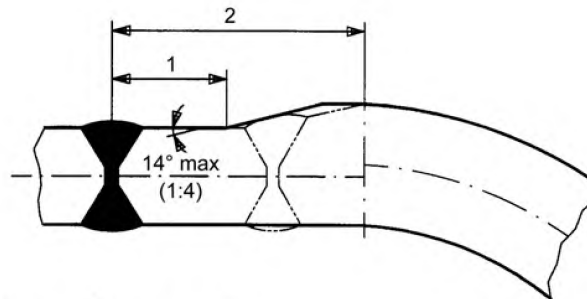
Стыковые сварные швы пластин разной толщины
